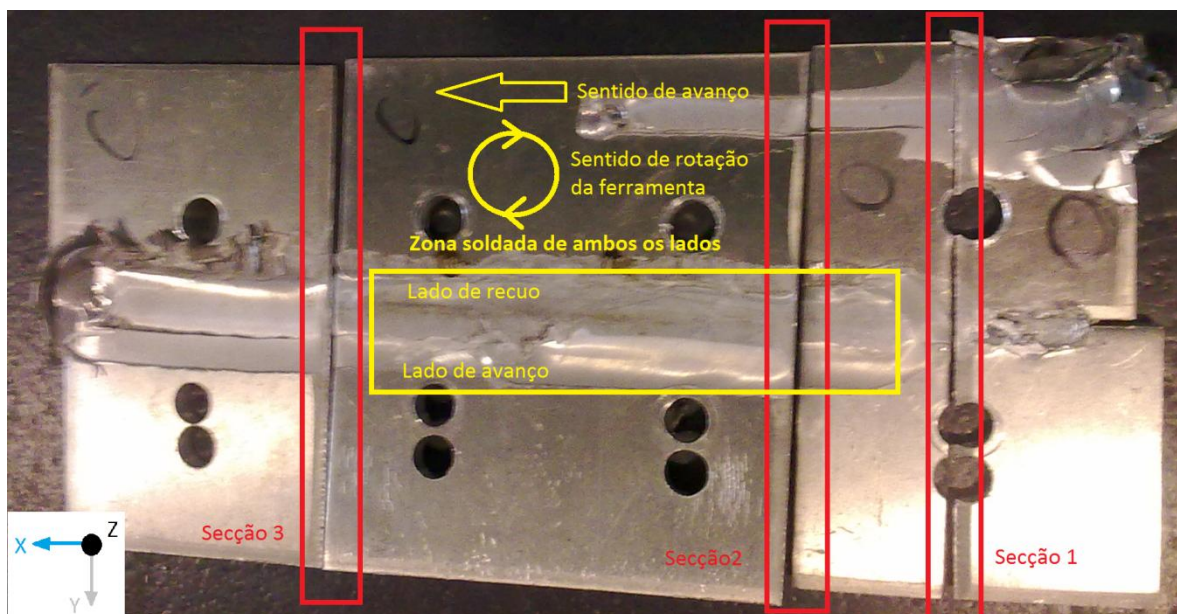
Parte superior do provete soldado de ambos os lados
